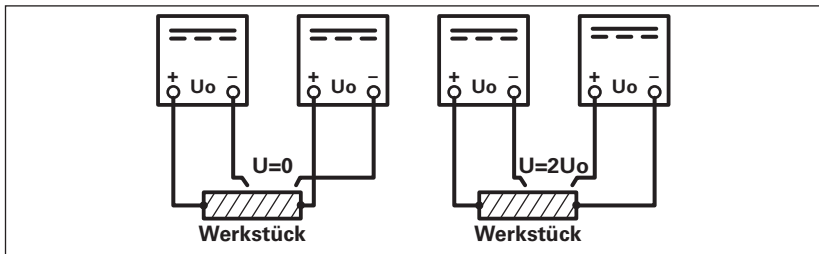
Die zum Schweißen gewählte Polung ist schweißtechnisch bedingt.
